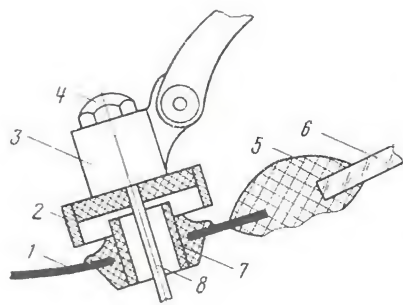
Узел в сборе: 1 — кузов; 2 — защитный колпачок; 3 — поводок; 4 — гайка; 5 — уплотнитель стекла; 6 — стекло; 7 — новая манжета; 8 — ось стеклоочистителя.
